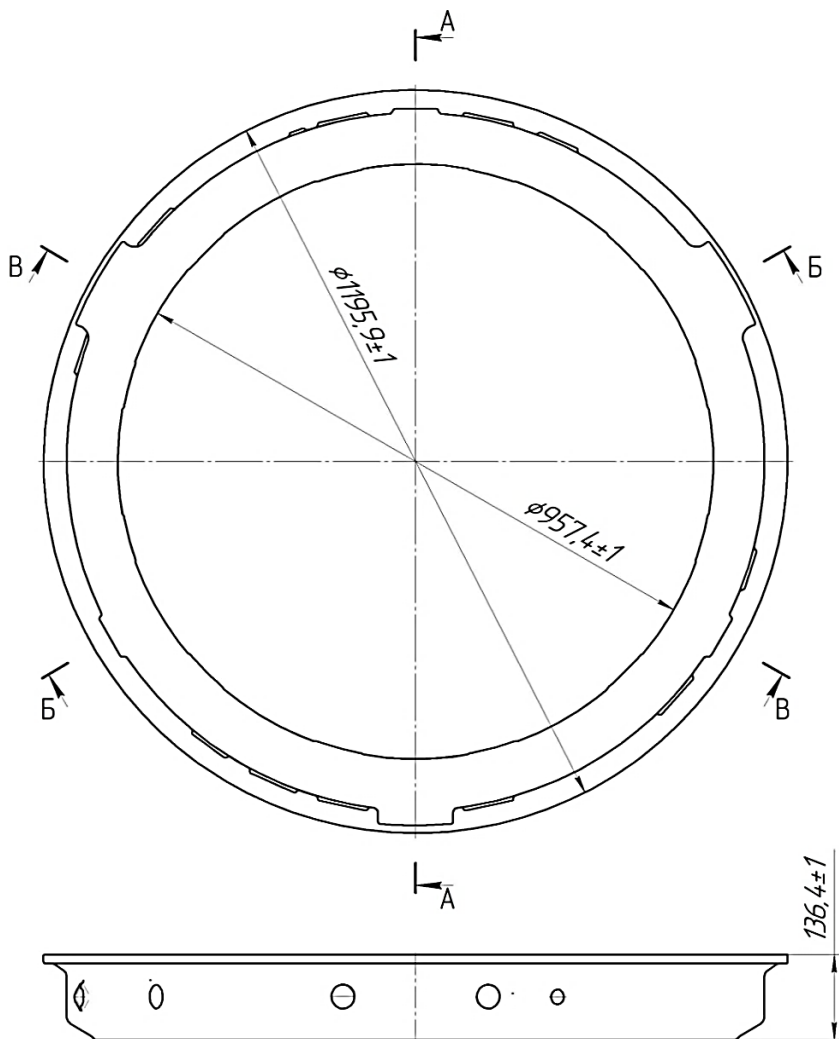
Схема измерения отливки детали «Корпус наружный»
